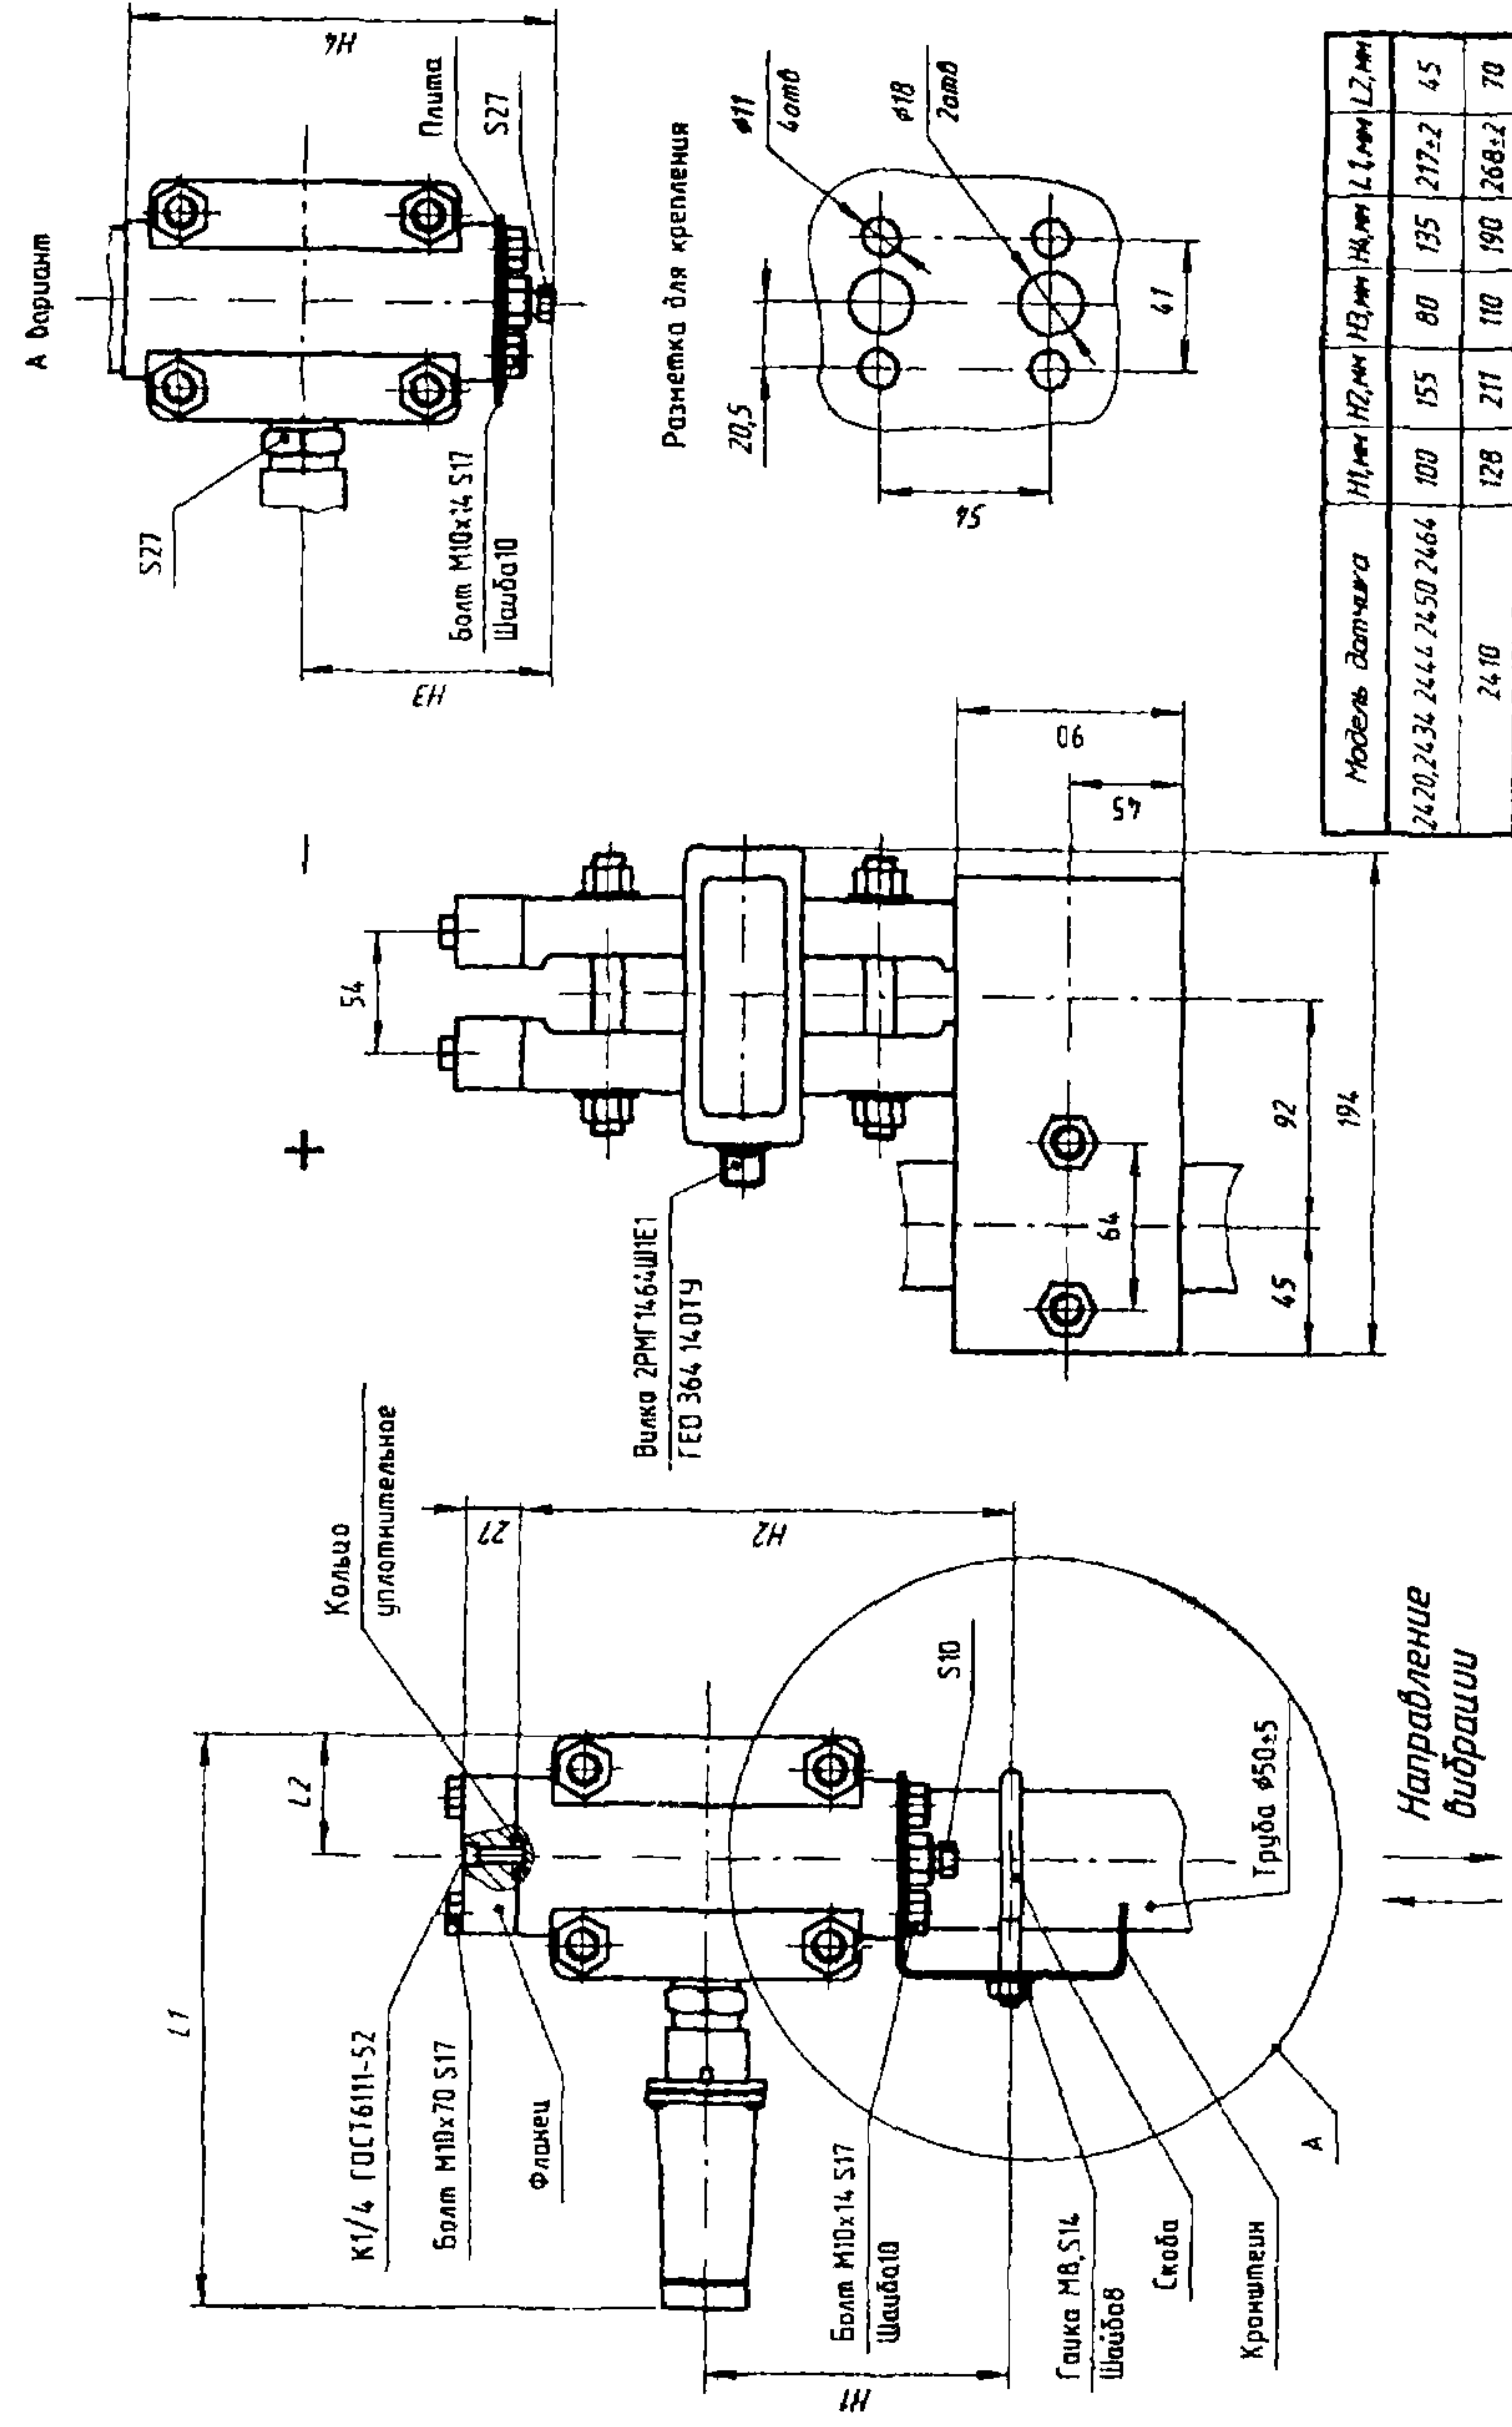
Установочные и присоединительные размеры датчиков моделей 2410, 2420, 2434, 2444, 2450, 2464 с установленными фланцами
